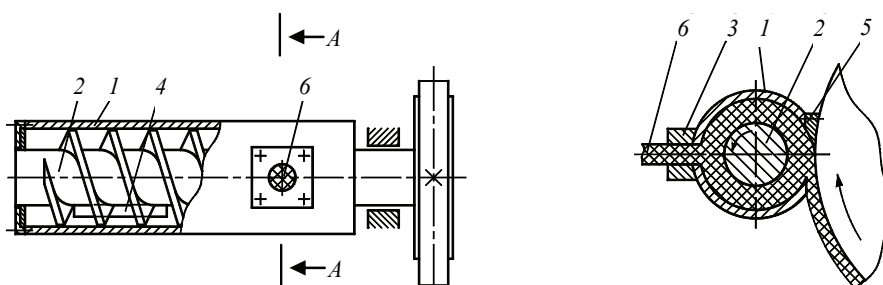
Схема шнекового отборочного устройства: 1 – цилиндр; 2 – шнек; 3 – формирующий инструмент; 4 – загрузочное окно; 5 – нож; 6 – расплав полимера
